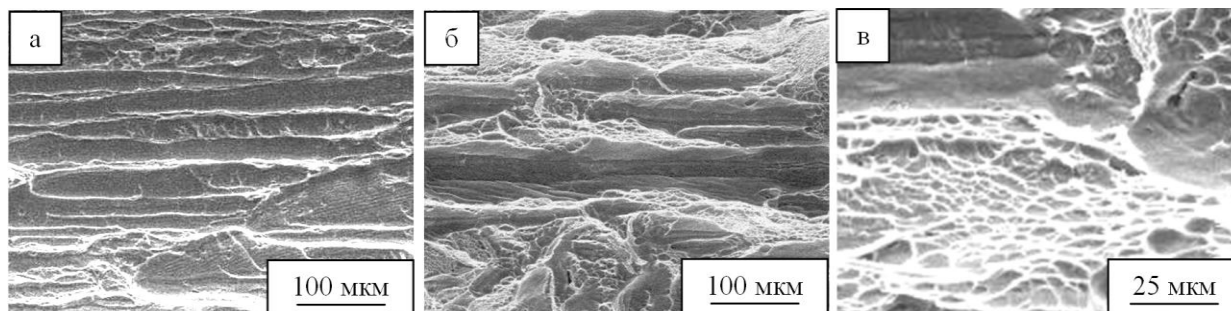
РЭМ-фрактограммы сварного соединения титанового сплава ВТ23 (метод ЛС). Малоцикловая усталость: (а) – волокнисто-полосчатый рельеф зоны ускоренного распространения трещины (образец без обработки); (б), (в) – волокнисто-полосчатый рельеф (образец после УЗК+ВЭВ) с большой долей вязкой ротационной составляющей в рельефе
